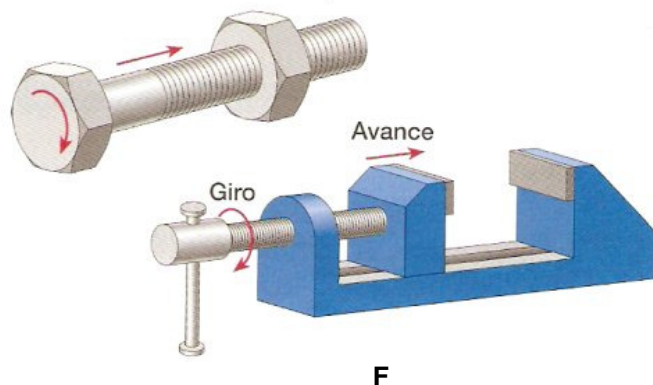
Mecanismo tornillo-tuerca. Fuente: www.TecnologiaIndustrialmiguel.com
